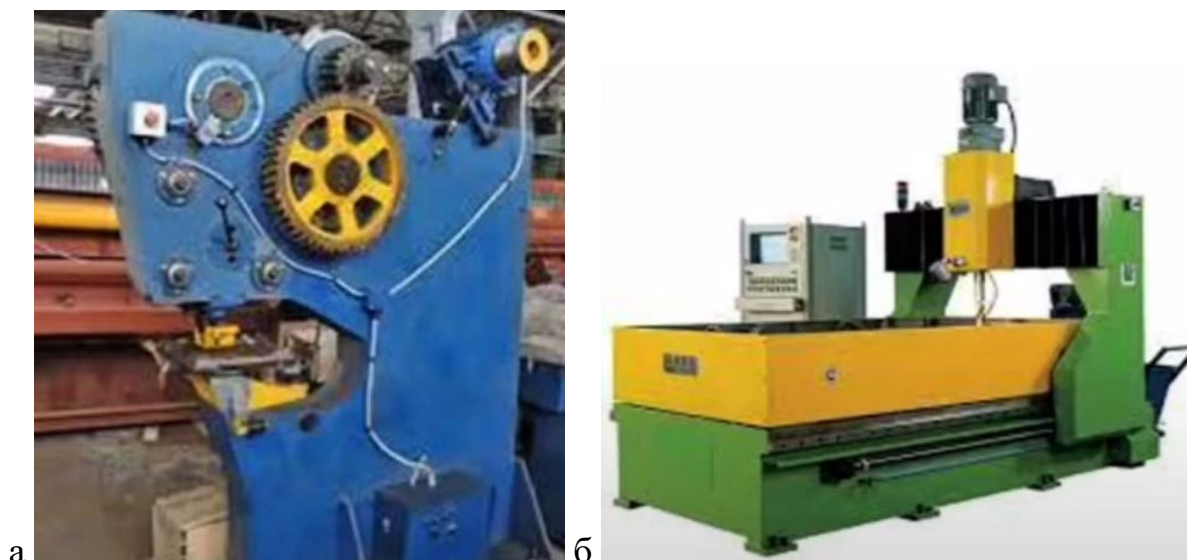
Прес для продавливання (а), свердильний верстат (б)
